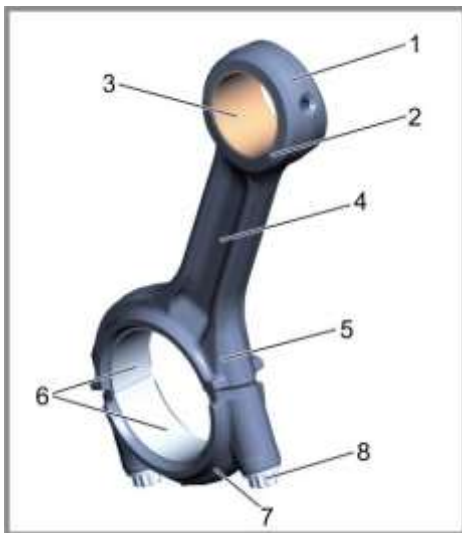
Шатун дизеля OM 473 вантажного автомобіля Mercedes-Benz: 1 – шатун; 2 – верхня головка шатуна; 3 – втулка верхньої головки; 4 – стрижень шатуна; 5 – нижня головка шатуна; 6 – підшипникова опора (вкладиші); 7 – кришка нижньої головки шатуна; 8 – болт
